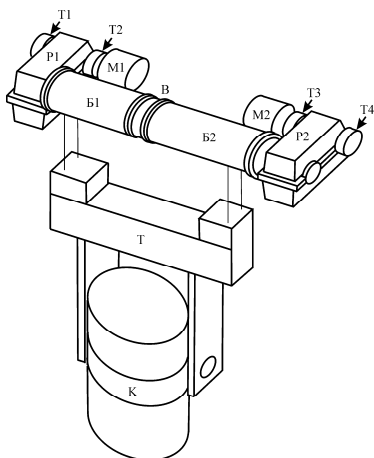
Схема механизма главного подъема крана: М1, М2 – приводные асинхронные двигатели; Р1, Р2 – редукторы; Б1, Б2 – барабаны; В – промежуточная вставка; Т – траверса; К – ковш (бадья)
